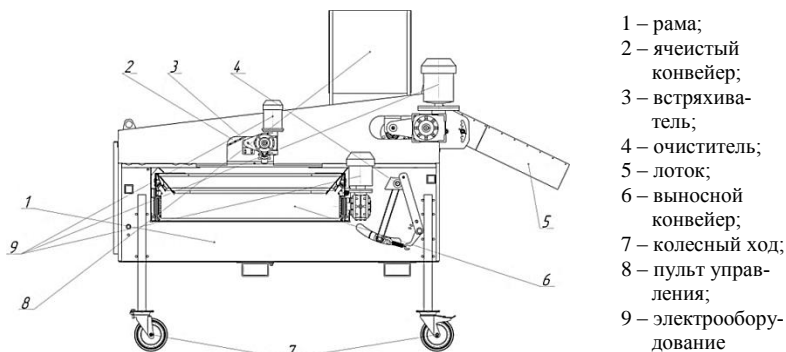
Схема машины МК-15 для калибровки картофеля
